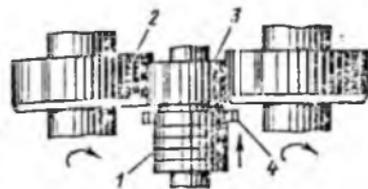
Накатка зубьев шестерен с осевой подачей заготовок
